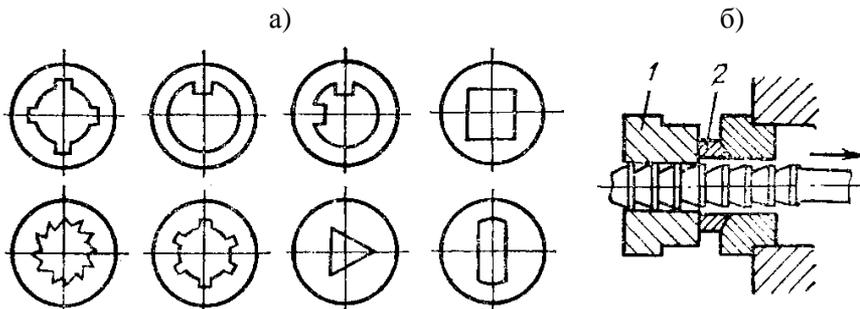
Формы протягиваемых отверстий (а) и схема обработки детали (б)
